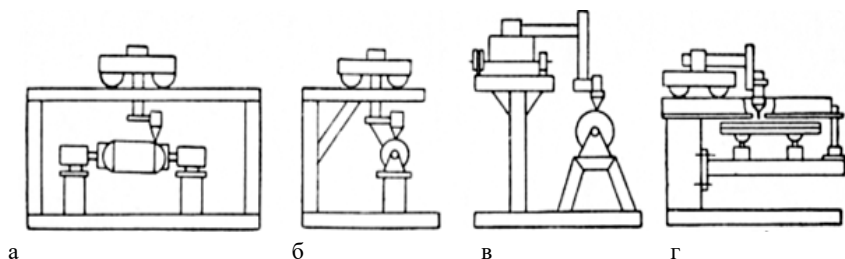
Типы сварочных установок для автоматической сварки плавлением:
